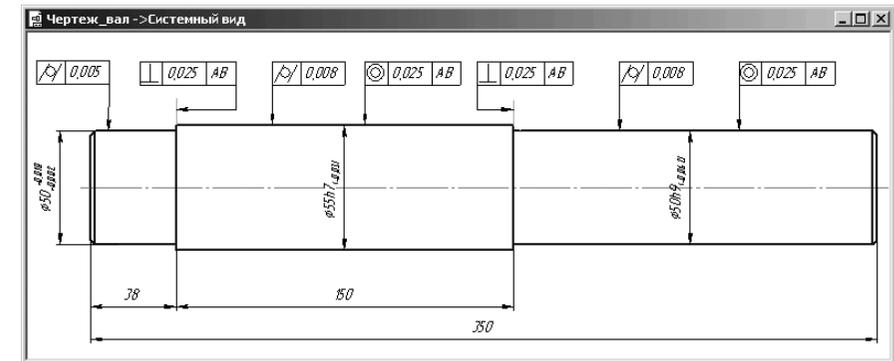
Знаки обозначения допусков форм поверхности для вала
